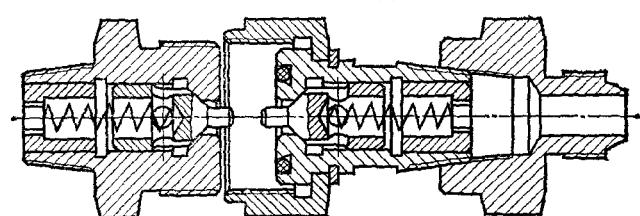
Примеры сборки резиновых рукавов со штуцером:
